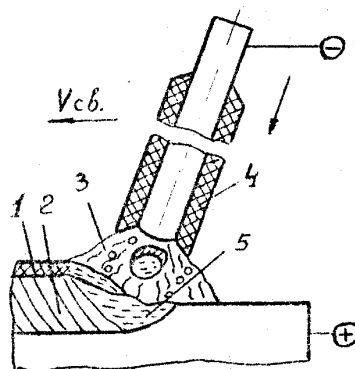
Схема ручной дуговой сварки металлическим покрытым электродом
